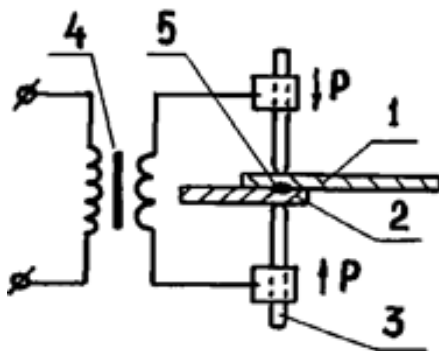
Принципиальная схема точечной сварки: 1, 2 – заготовки; 3 – электроды; 4 – трансформатор; 5 – сварочная точка
